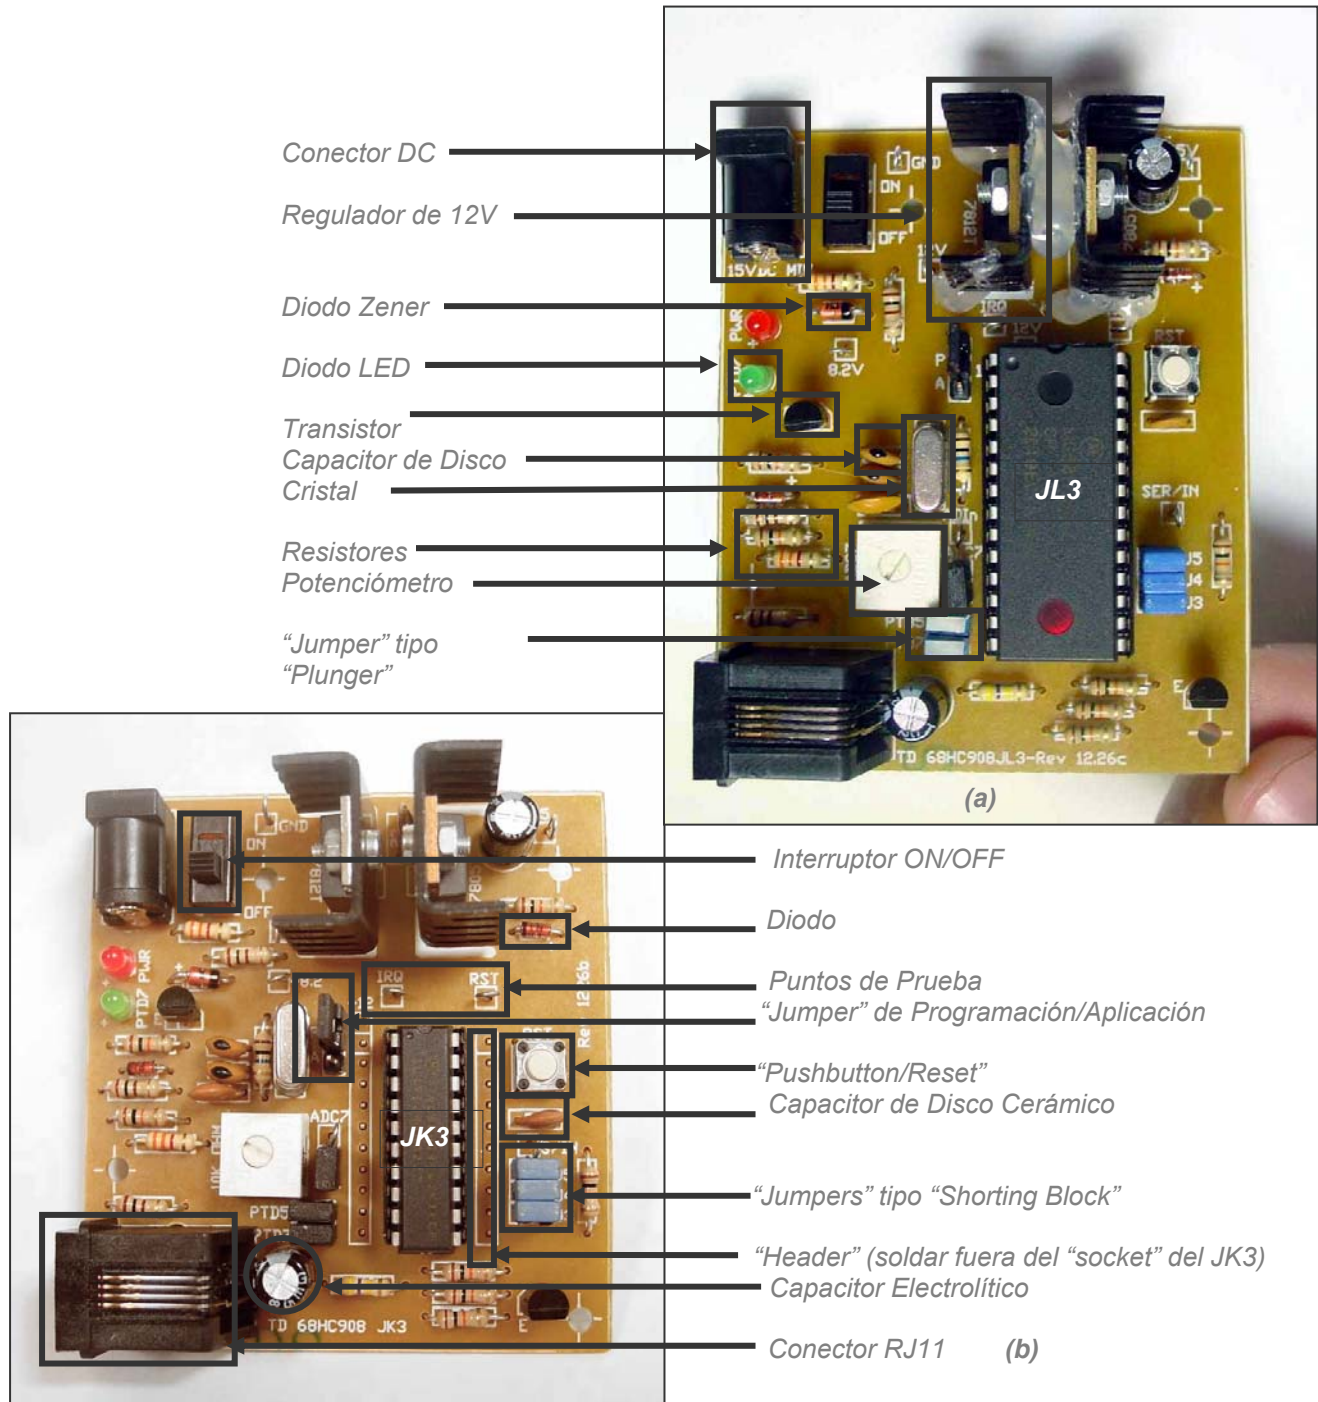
Tarjetas de Desarrollo. (a) TD68HC908JL3. (b) TD68HC908JK3. Usar como referencia al momento de soldar y comparar componentes con la tarjeta a armar.
